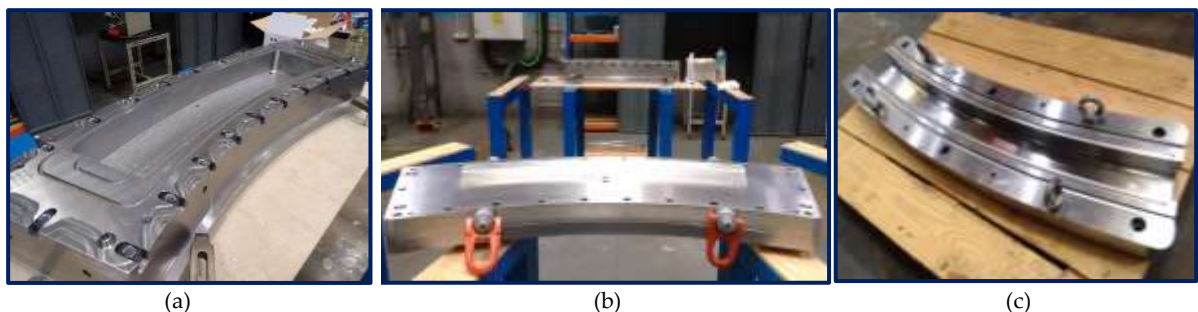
Molde de RTM de la cuaderna en U: (a) parte inferior del portamoldes, (b) parte superior del portamoldes junto con el postizo convexo de aluminio y (c) convexo cóncavo de acero.
